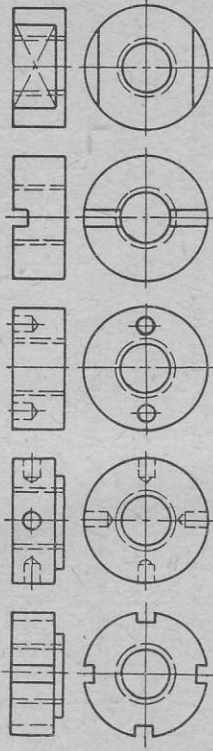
Obr. 62. Obr. 63. Obr. 64. Obr. 65.
